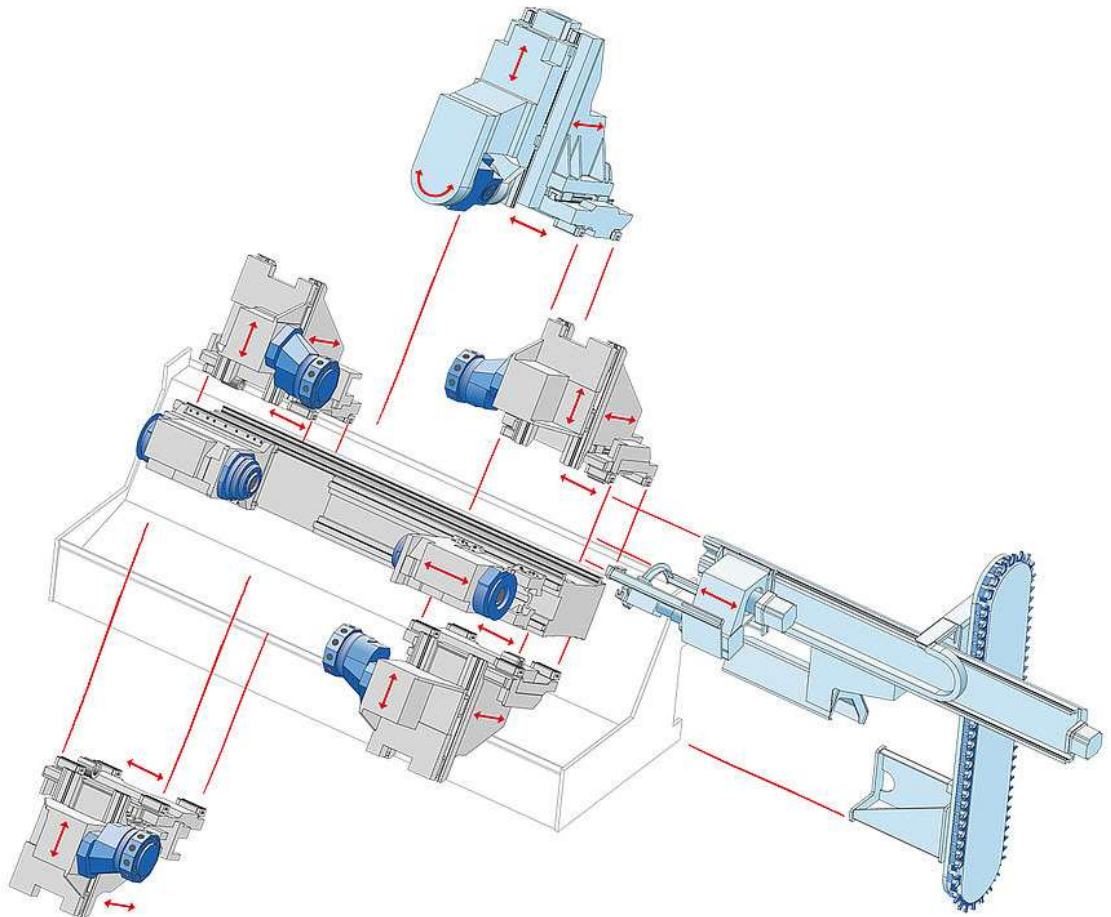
Модульна структура серії токарних верстатів з ЧПК TNX 80/65 фірми TRAUB для двосторонньої багатоінструментальної обробки
